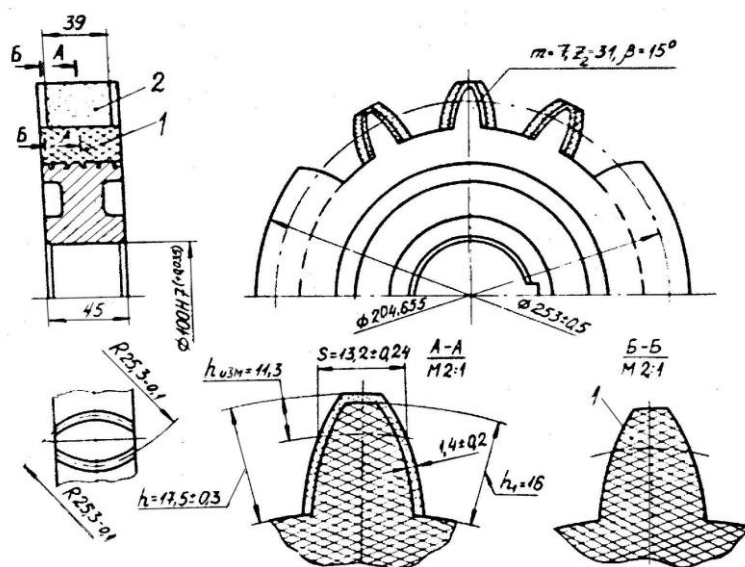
Инструмент для калибровки сферических зубчатых колес
